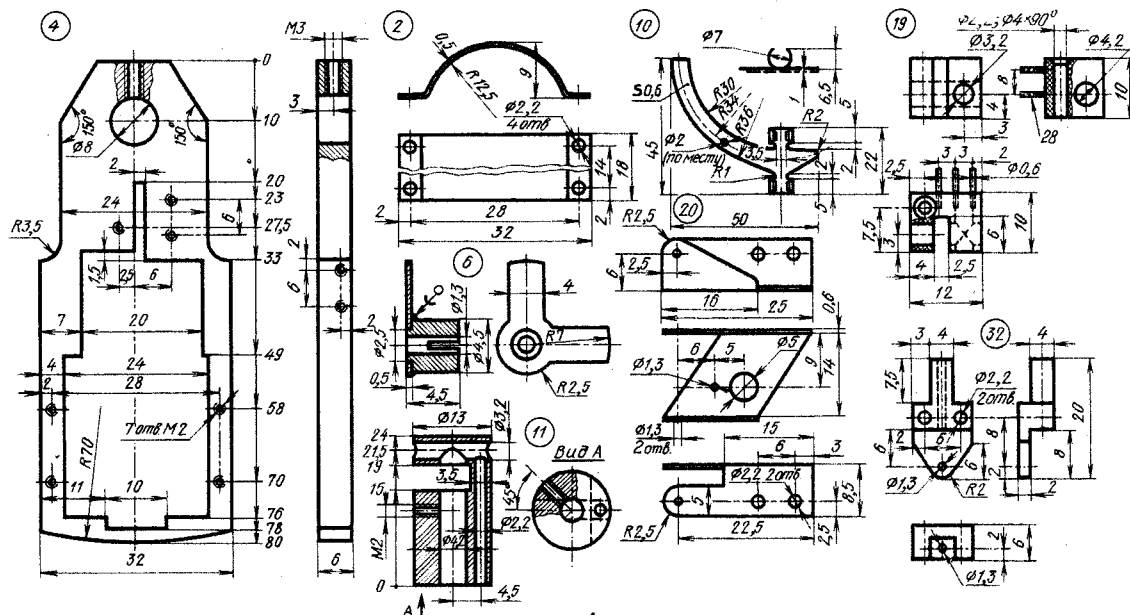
Детали механизма: 2 — скоба, Л62, никелировать; 4 — кронштейн, Д16-Т, полировать; 6 — шторка, Л62, втулку паять припоем ПОС-40; 10 — пластина, Бр. КМц3-1, никелировать, резиновую прокладку (показана штриховой линией)
